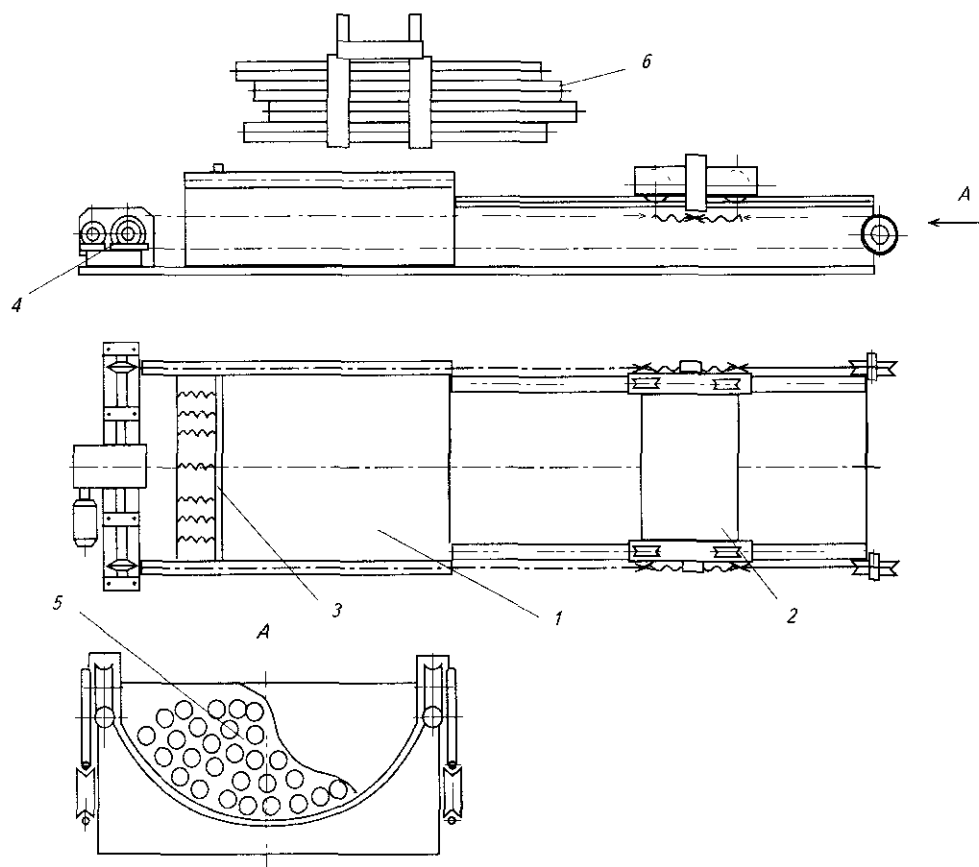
Торцеватель бревен с одной неподвижной стенкой конструкции АО «Союзлесмонтаж»:
